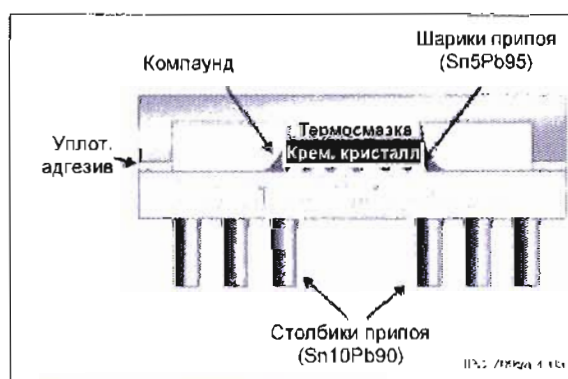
Керамический корпус BGA со столбиковыми выводами в разрезе
